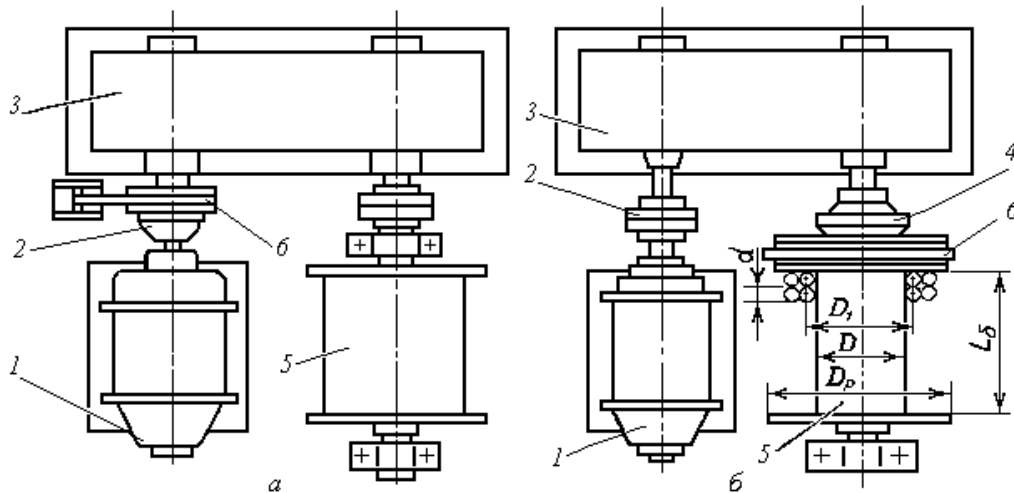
Типы лебедок: *а* – подъемная; *б* – транспортная; 1 – двигатель; 2 – муфта соединительная; 3 – редуктор; 4 – муфта включения; 5 – барабан; 6 – тормоз
